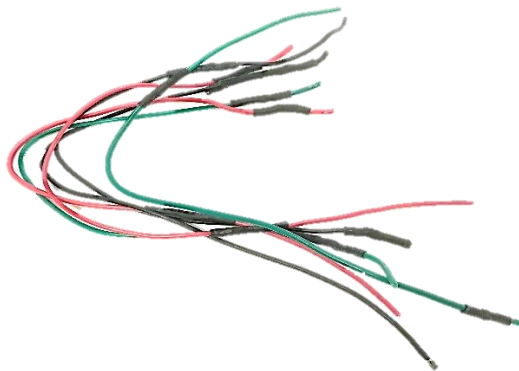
Fios de ligações com vários pontos de soldadura.
